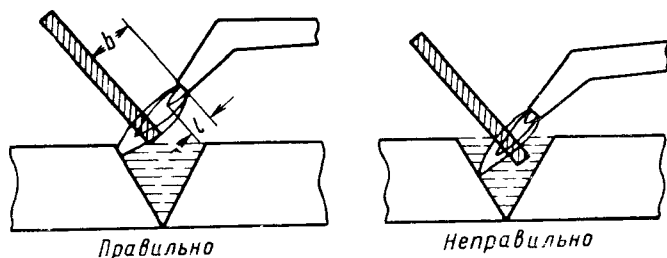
Расположение присадочного прутка по отношению к расплаву шва
